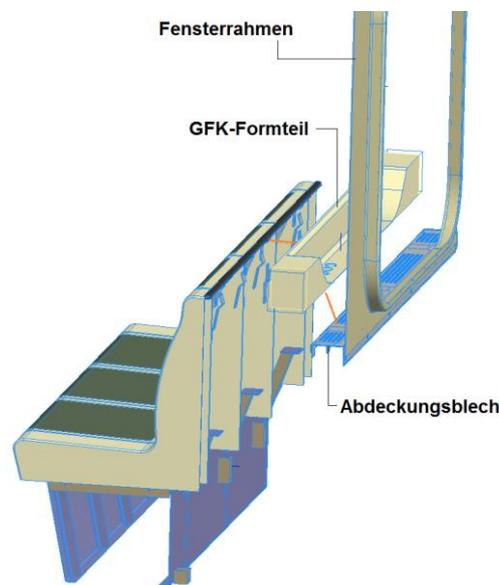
Explosionsansicht; GFK-Formteil aktuell
